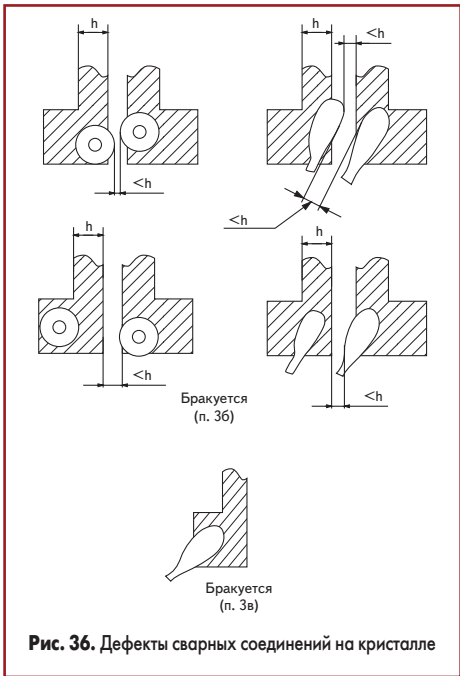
Дефекты сварных соединений на кристалле
